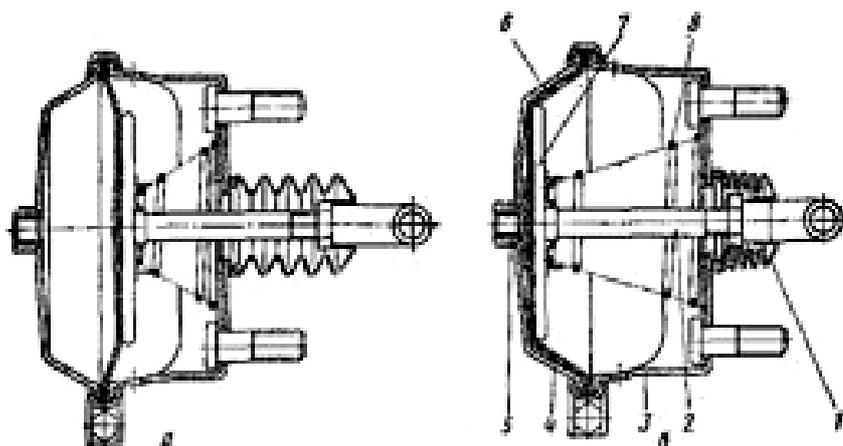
Тормозная камера типа 24: а-отторможенное положение; б-положение при торможении; 1-защитный чехол, 2-шток, 3-корпус, 4-крышка, 5-штуцер, 6-диафрагма, 7-опорный диск, 8-пружина
